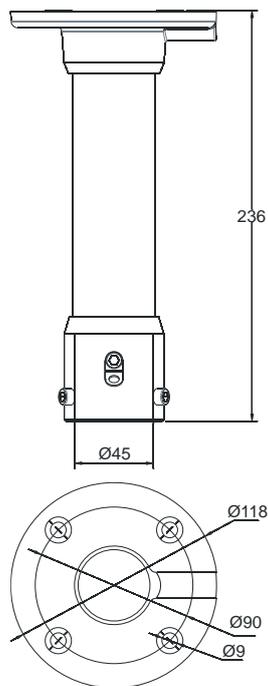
Immagine delle dimensioni del braccio di installazione a soffitto
